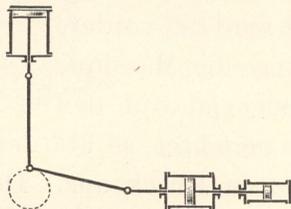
Dreifach-Expansionsmaschine. (Hochdruck- und Mitteldruckzylinder liegend, Niederdruckzylinder stehend, sämtlich auf eine Kurbel arbeitend.)
